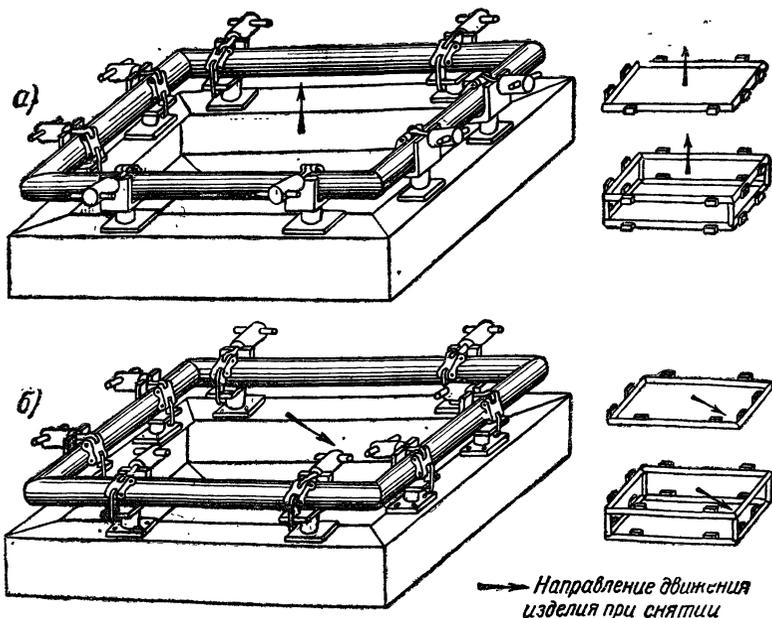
Устранение конструктивных недостатков приспособлений для прихватки мелких деталей.
